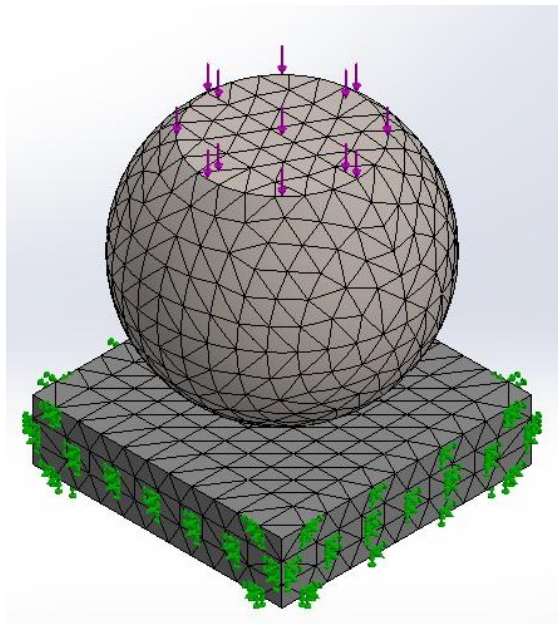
Ensamblaje bola-plano utilizado en SolidWorks
